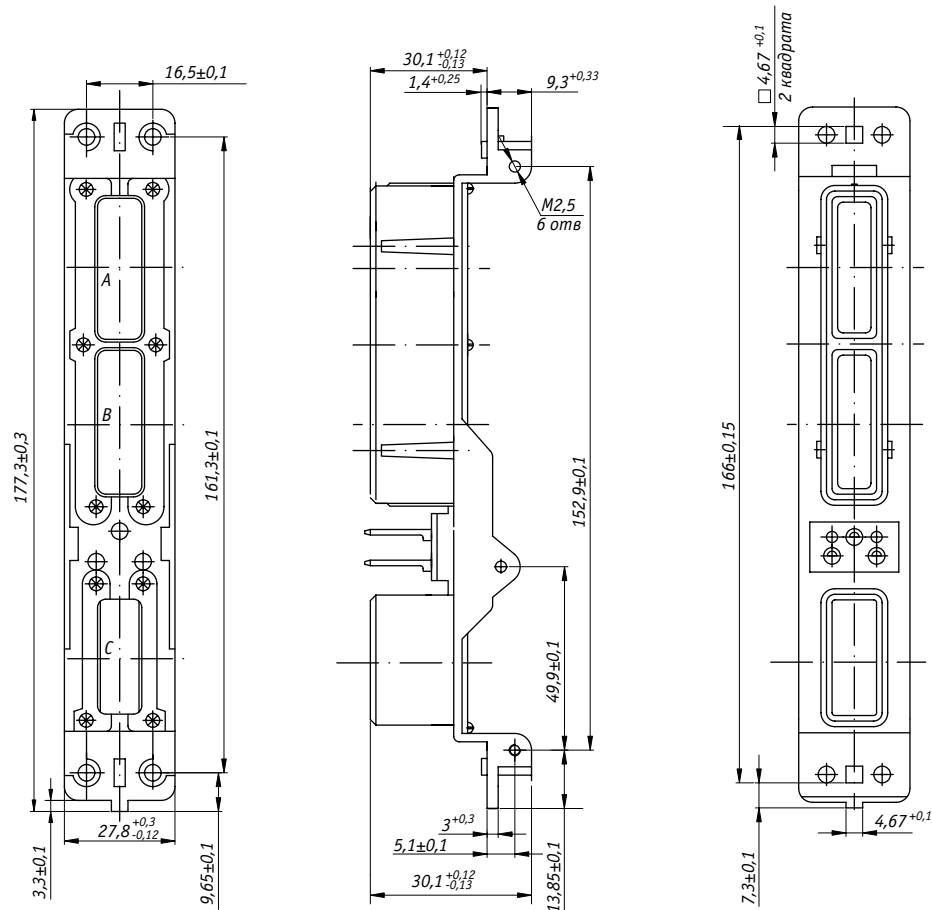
Корпус вилок 1 типоразмера для номеров схем расположения изоляторов в корпусе 101...107 (см. таблицу 3)
